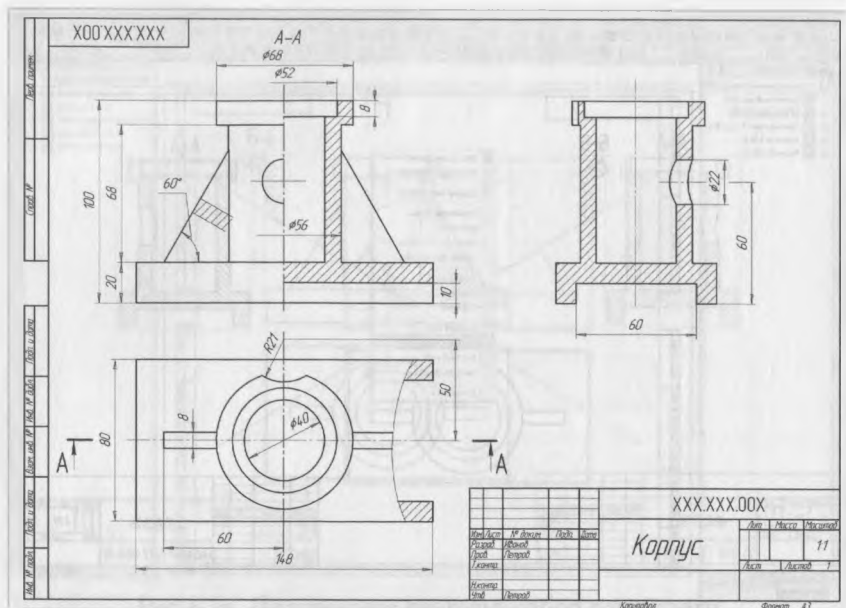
Чертеж детали с ребрами жесткости в КОМПАС-3D
